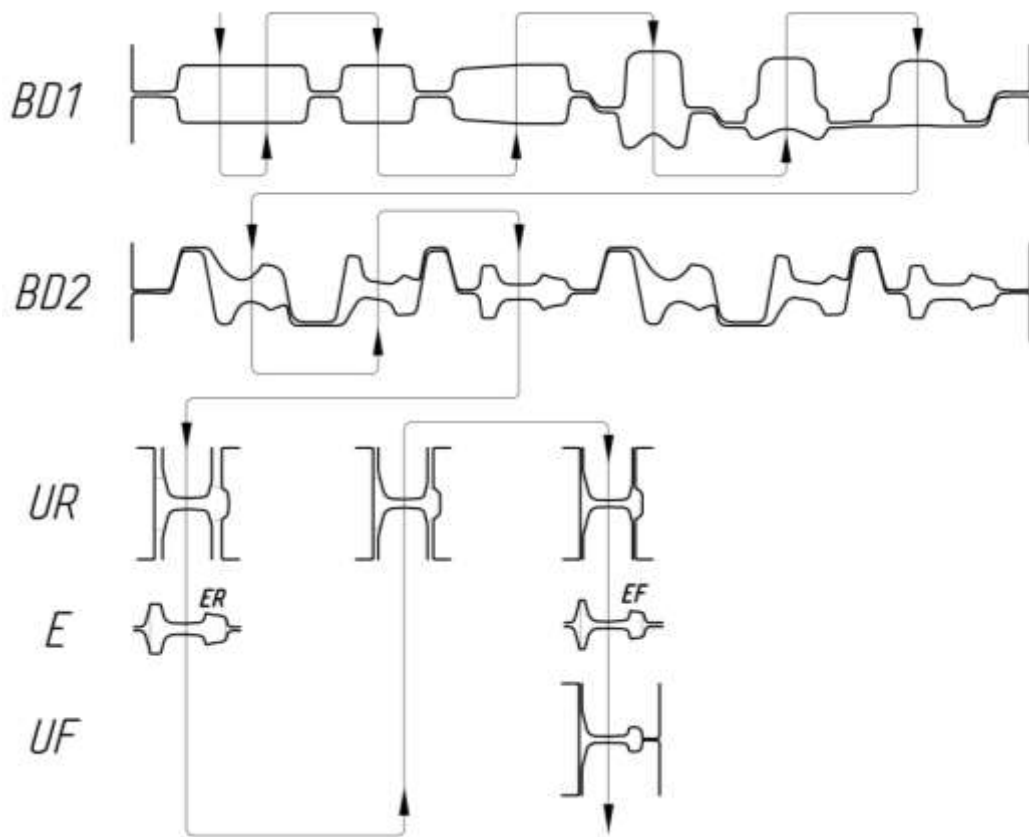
Схема калибровки для прокатки рельсов с резкой заготовки в трапецевидном калибре
